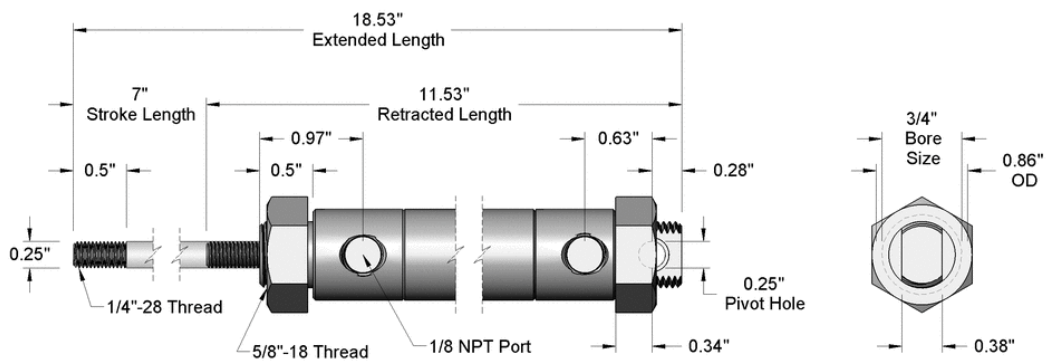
Dimensión de cilindro seleccionado A y B.
